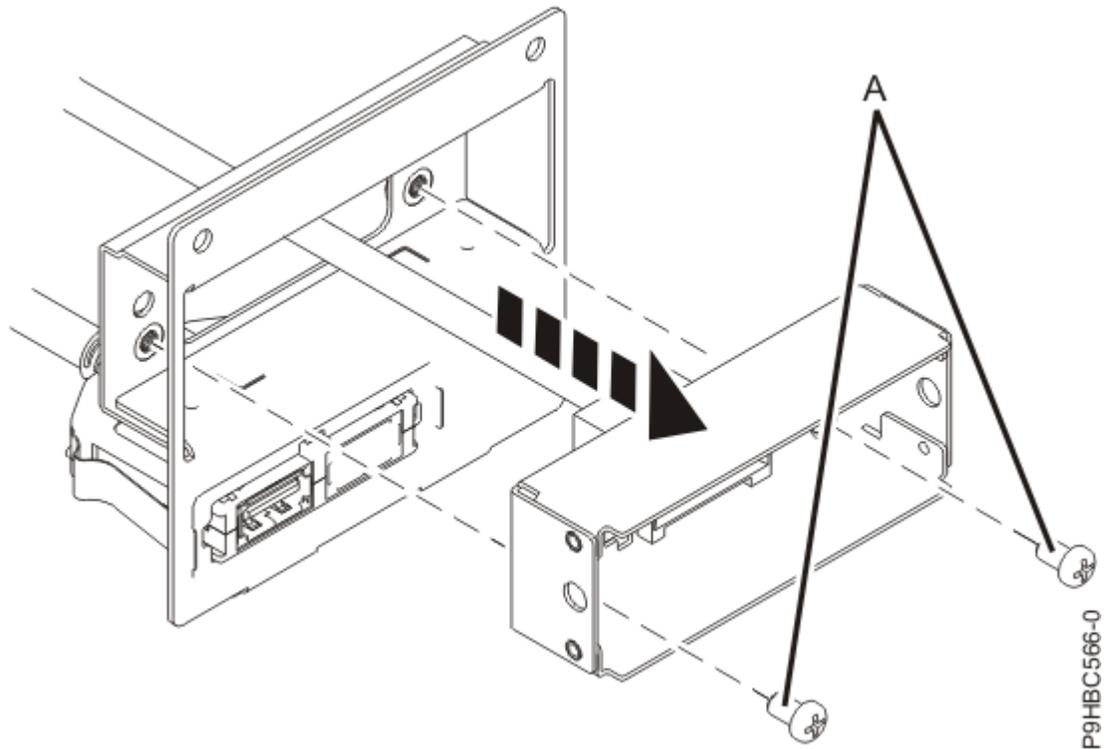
Remova o cabo do ecrã do painel de controlo da caixa para um sistema montado em bastidor
